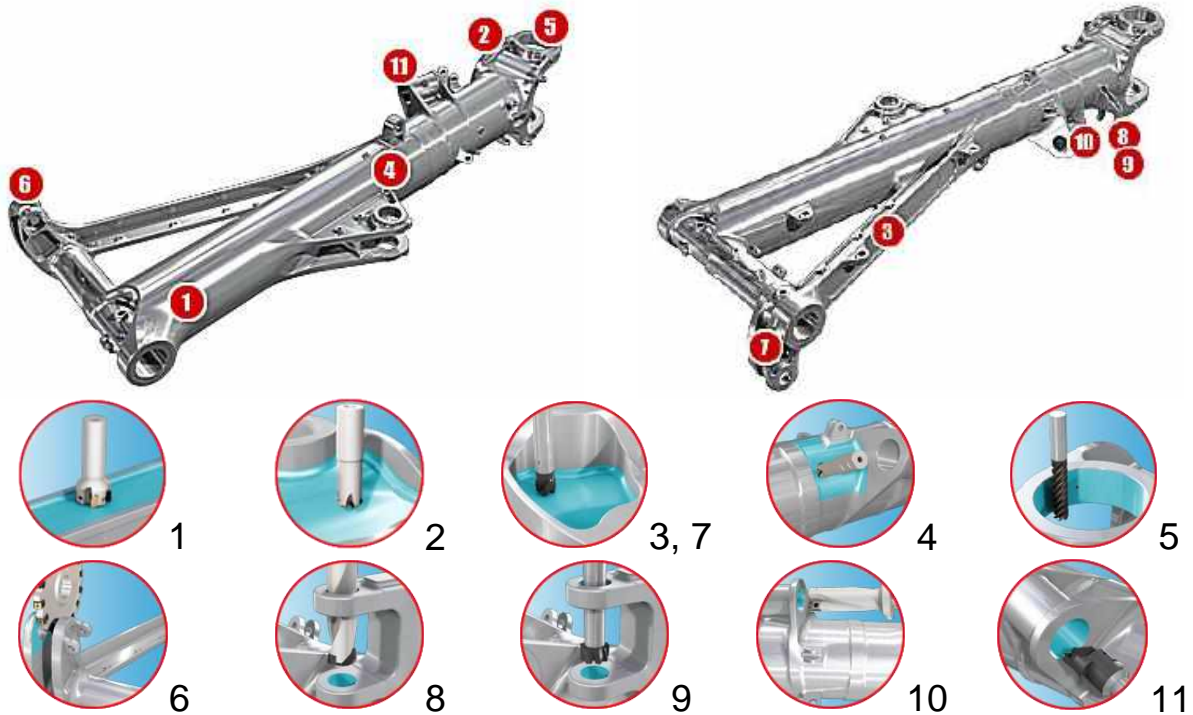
Схема послідовності оброблення поверхонь заготовки стояка шасі:
